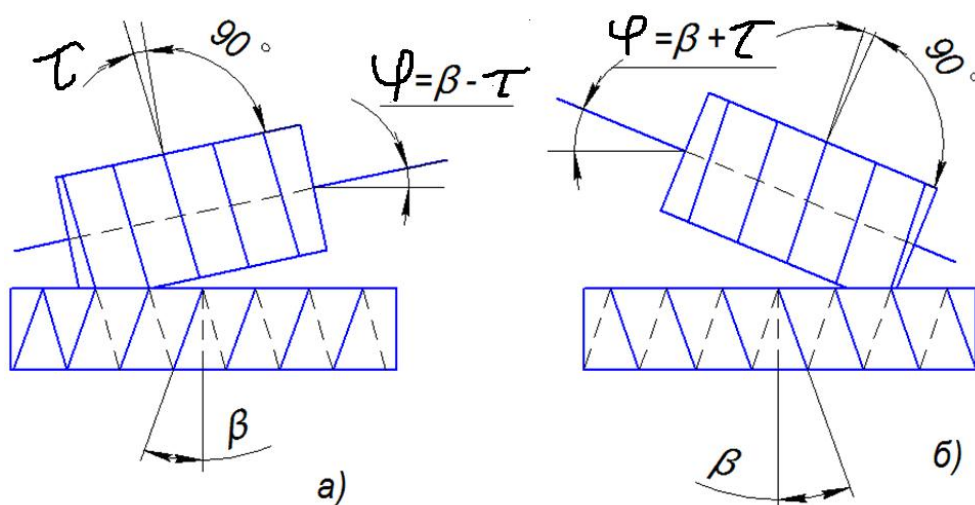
Схема нарезания косозубых колес червячными фрезами
